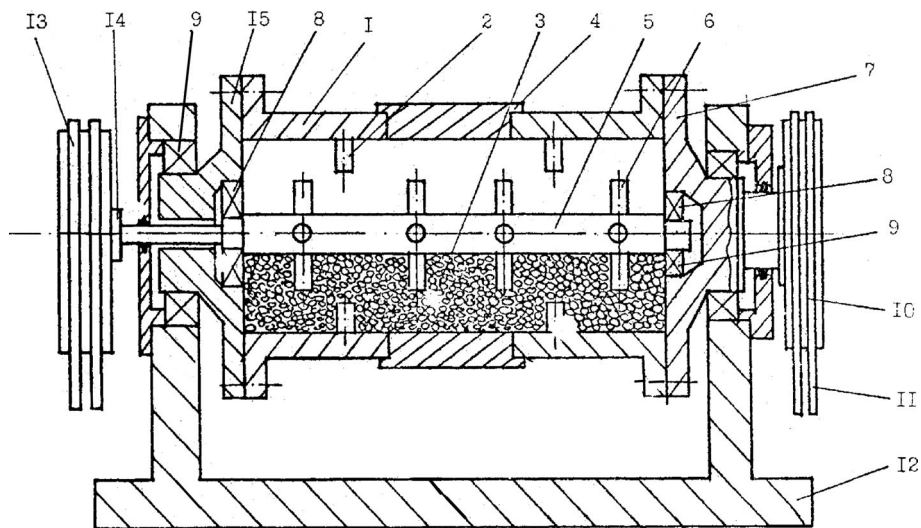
Аттритор с горизонтальной осью вращения: 1 — горизонтальный барабан; 2, 6 — лопасти; 3 — размольные тела; 4 — люк; 5 — импеллер; 7, 15 — корпус; 8, 9 — подшипники качения; 10, 14 — шкив; 11, 13 — клиноременная передача; 12 — станина
